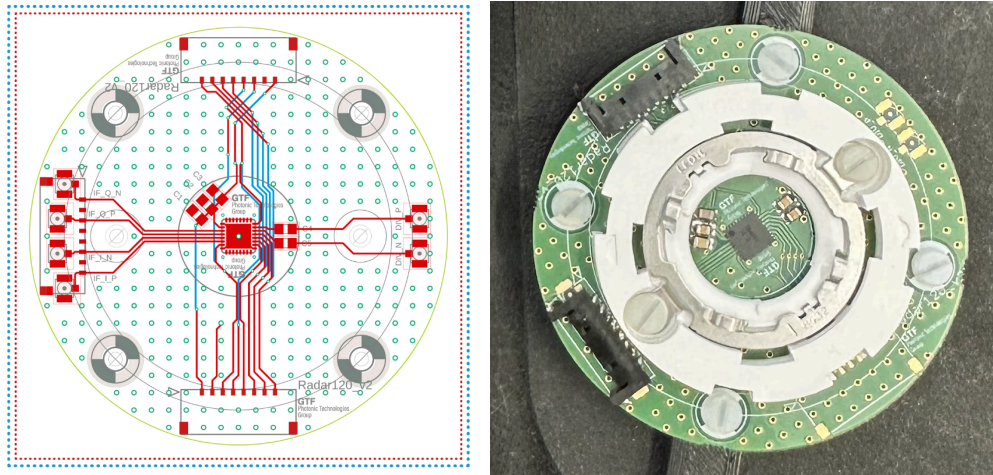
A la izquierda, esquemático de la placa donde soldaremos el radar, a la derecha, placa final con el radar y las conexiones soldadas
